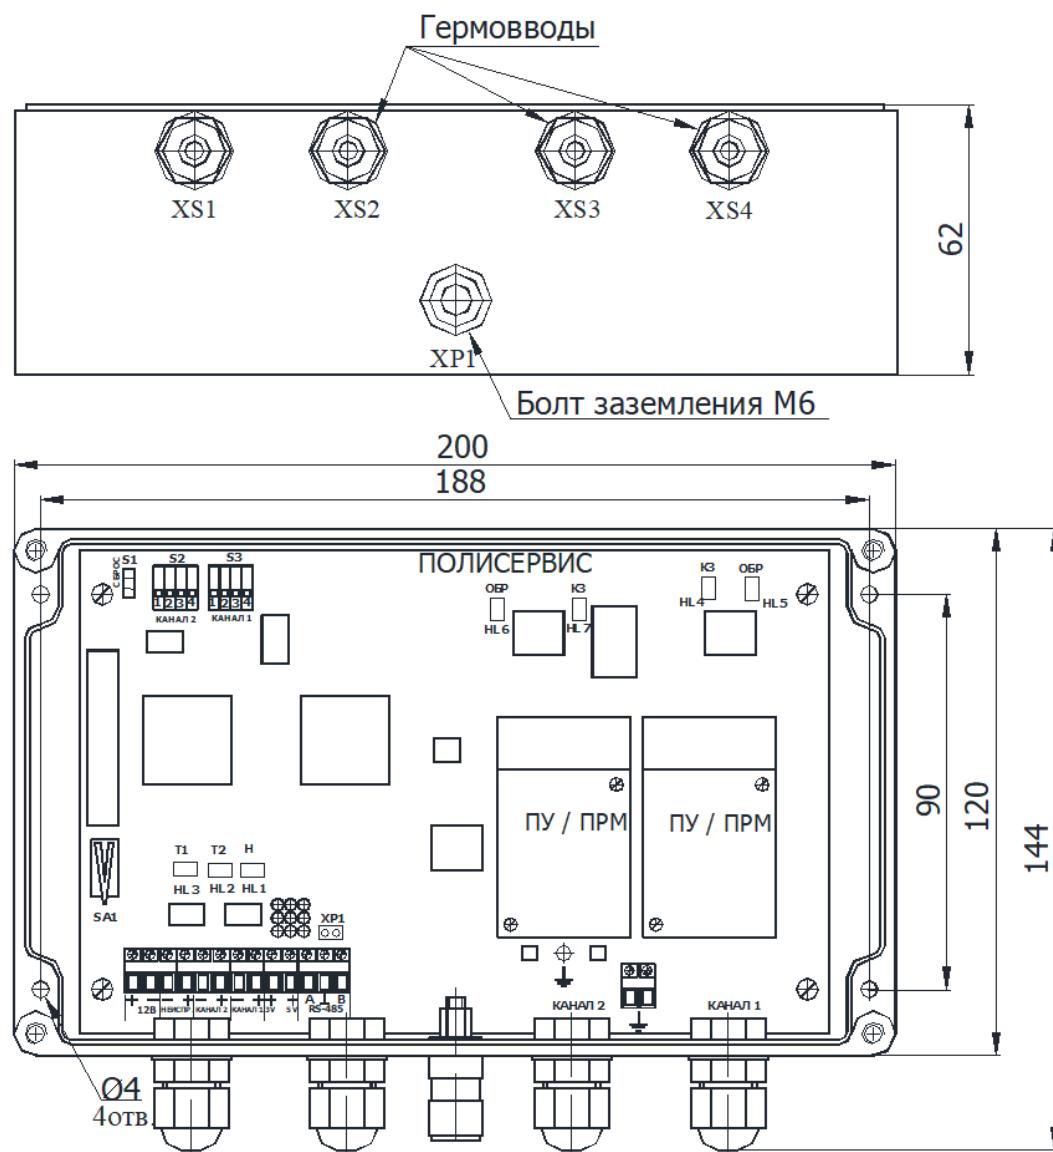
Общий вид БОС-1 в корпусе из поликарбоната
